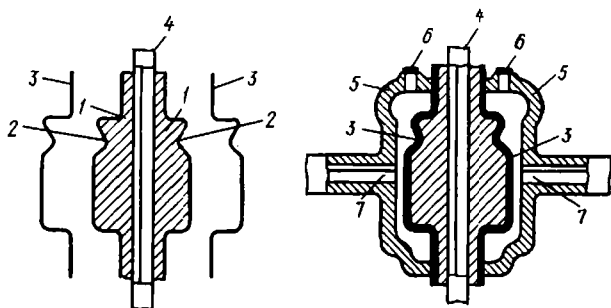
Схема формирования облицовки из сыпучего материала на основе V-процесса: 1 — модель; 2 — рабочая поверхность модели; 3 — пленка; 4 — труба для присасывания пленки к поверхности модели; 5 — кокиль; 6 — отверстие с заглушкой для подачи зернистого формовочного материала; 7 — труба для вакуумирования полости облицовки
